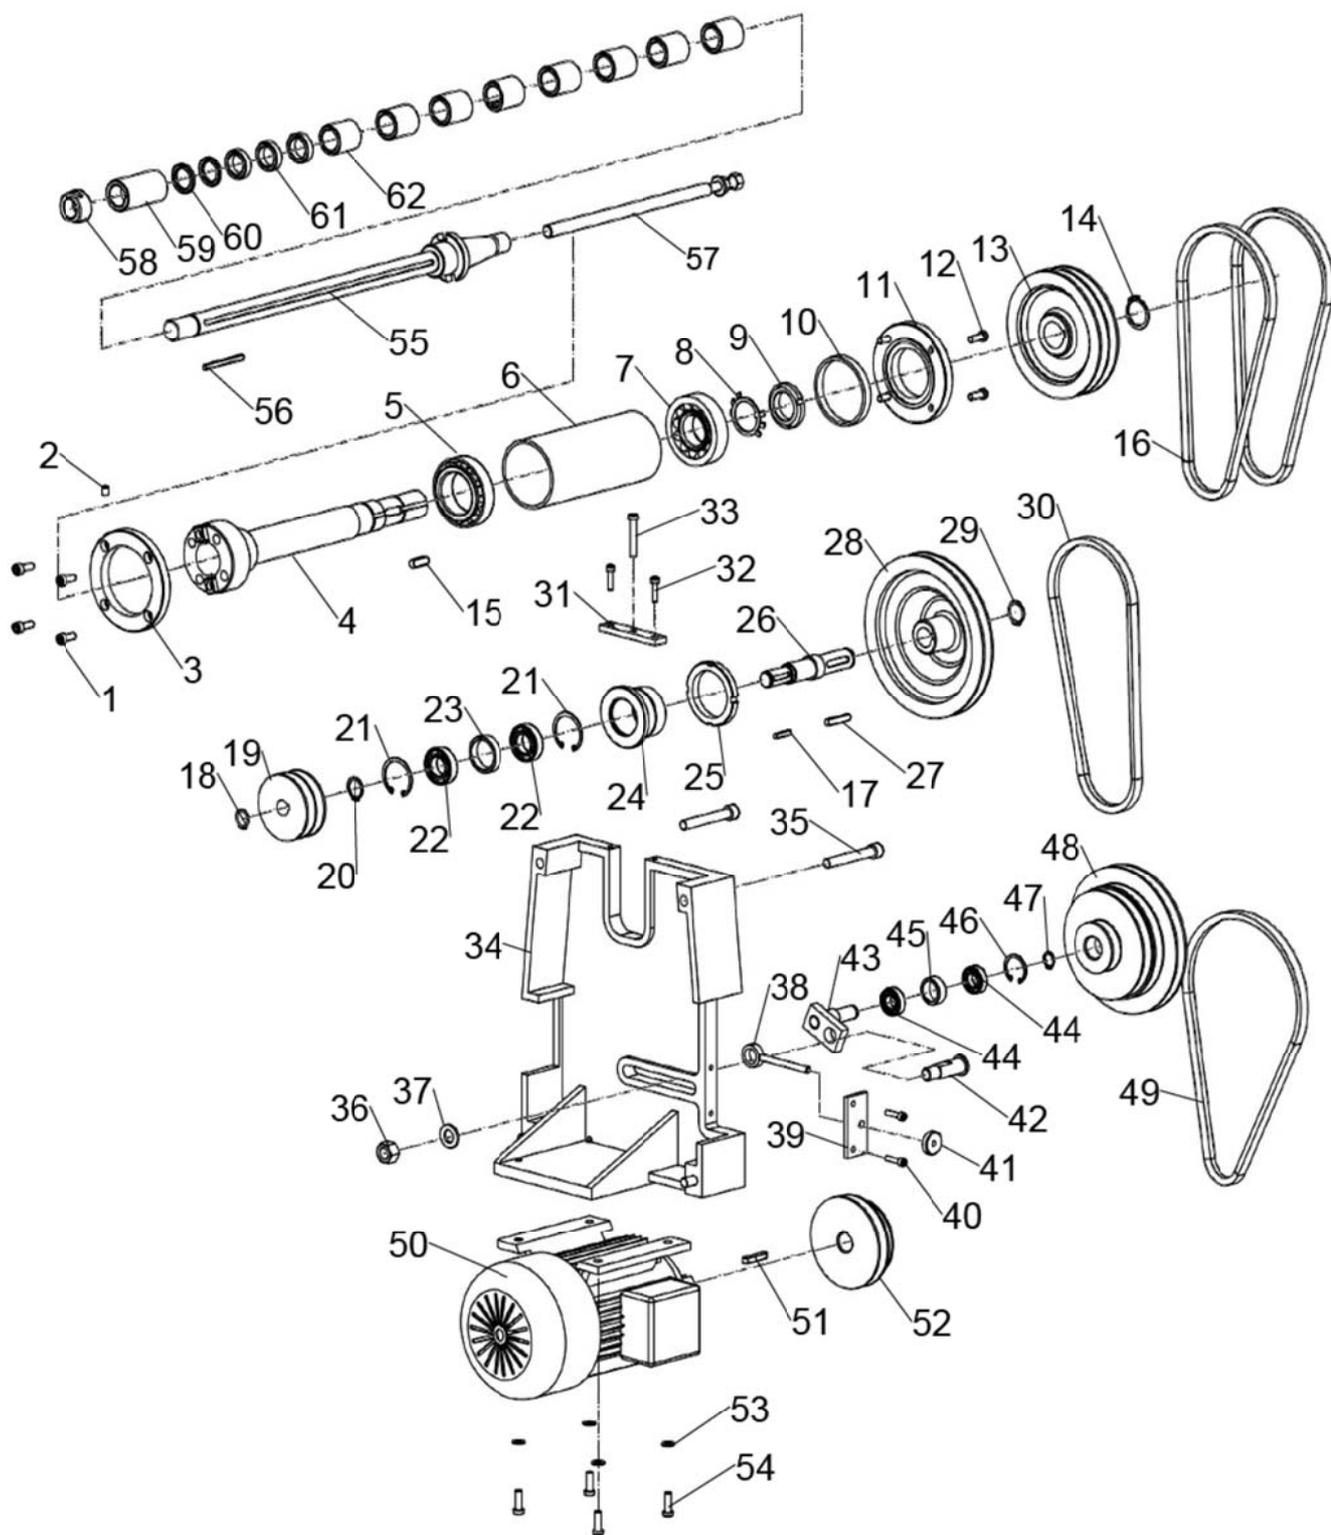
Riementrieb Horizontalfräsen - Belt drive horizontal milling
